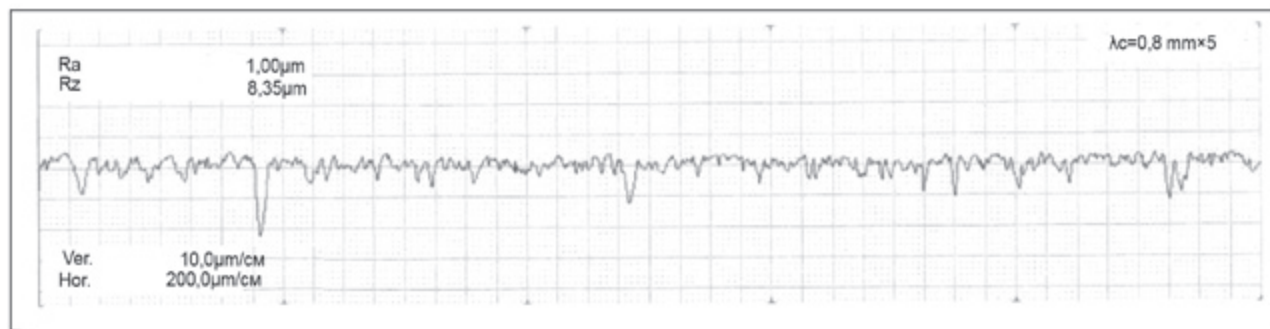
Профиль шероховатости привалочной поверхности ДВС на ЯМЗ
